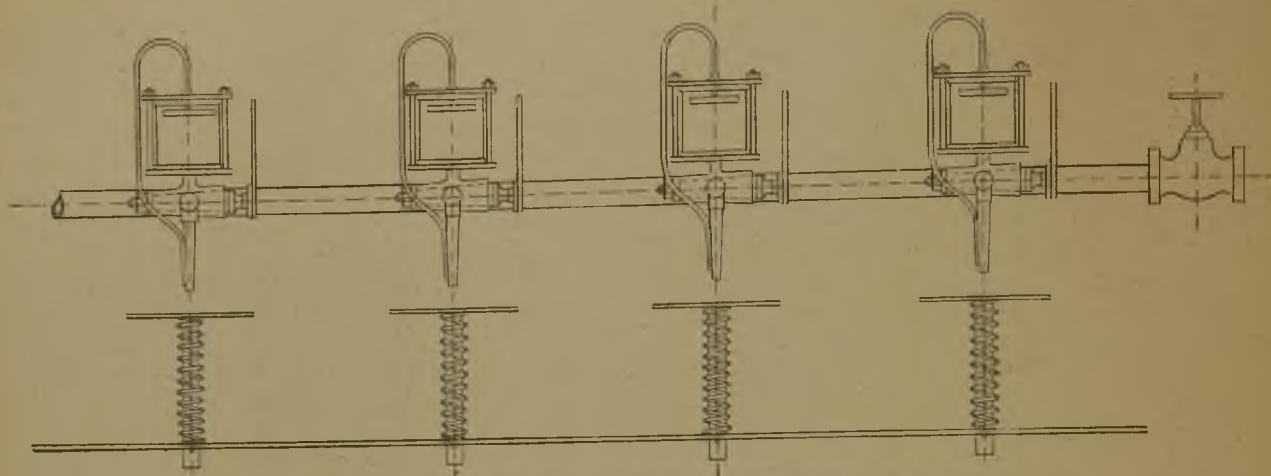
Seippelsche Gruppen-Füllvorrichtung für Lampentöpfe.
